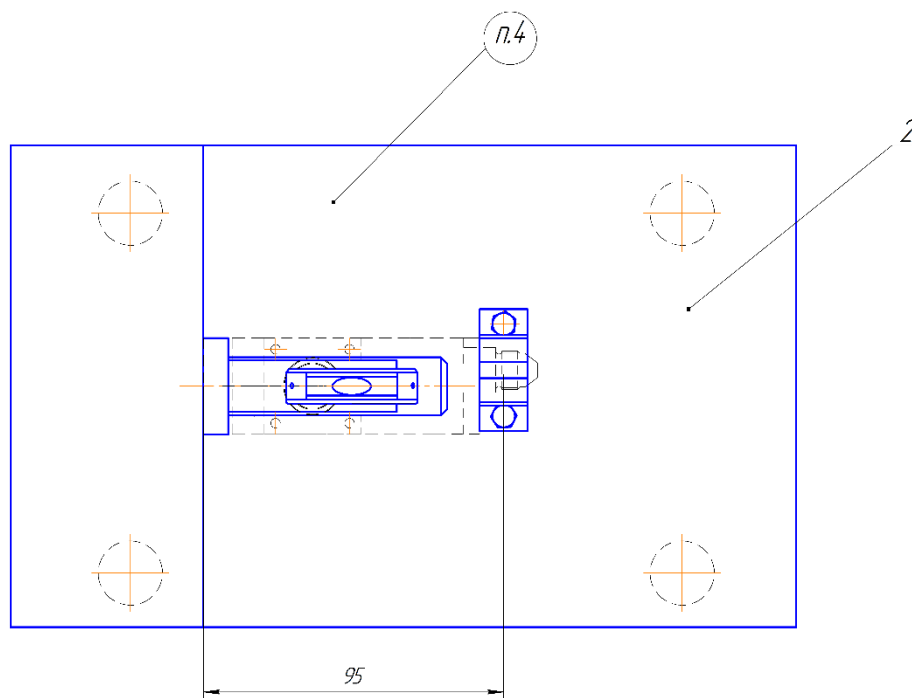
Контрольно–измерительное приспособление вид сверху
